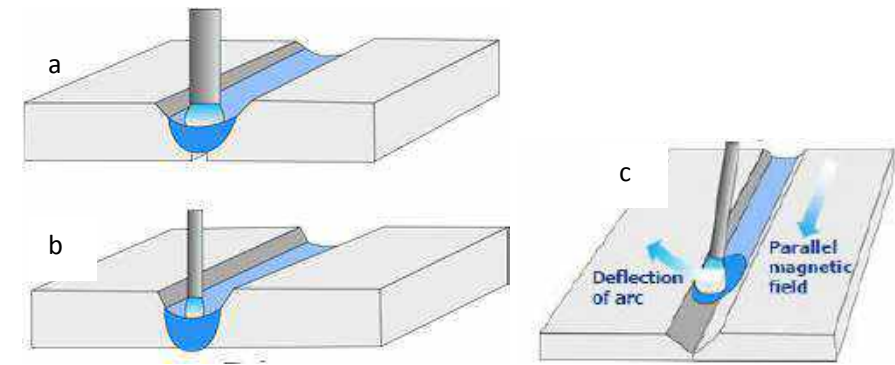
incomplete root penetration pada lasan baja (TWI, 2018)
